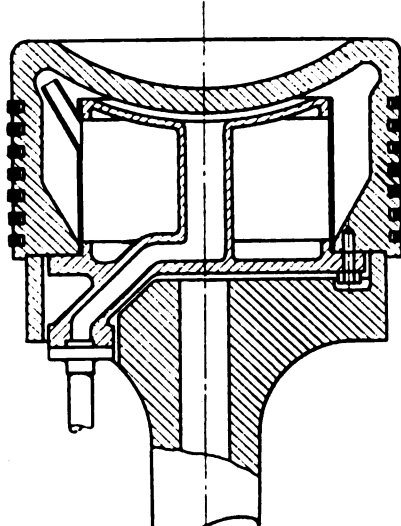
und 9. Moderne Kolbenkonstruktionen für Viertaktmaschinen mittlerer Größe
